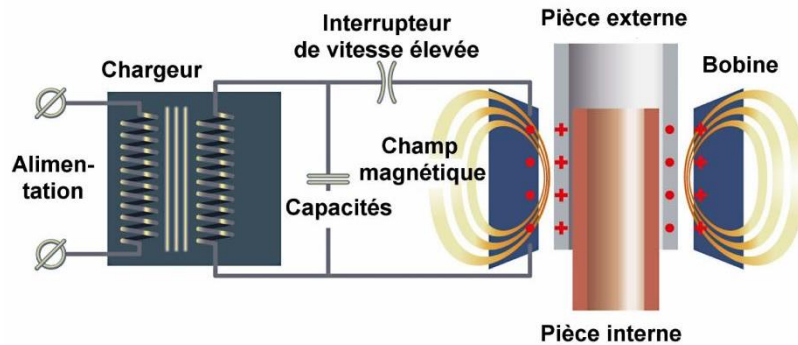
Processus de soudage par impulsion magnétique [5].
